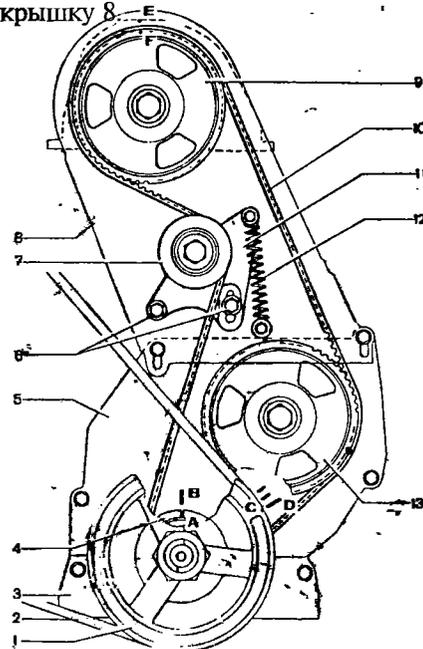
Схема привода распределительного вала: 1 - шкив коленчатого вала; 2 - ремень привода генератора; 3 - нижняя защитная крышка; 4 - зубчатый шкив коленчатого вала; 5 - средняя защитная крышка; 6 - болты, крепления кронштейна натяжного ролика; 7 - натяжной ролик; 8 - верхняя защитная крышка; 9 - шкив распределительного вала; 10 - зубчатый ремень; 11 - кронштейн натяжного ролика; 12 - пружина кронштейна; 13 - шкив валика привода масляного насоса; А - метка на зубчатом шкиве коленчатого вала; В, D - метки ВМТ на крышке привода распределительного вала; С - метка на шкиве коленчатого вала; Е - метка на крышке головки цилиндров; F - метка на шкиве распределительного вала
